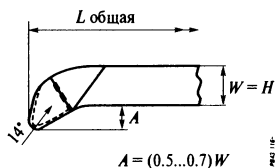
Резьбонарезной резец для нарезки наружной резьбы
